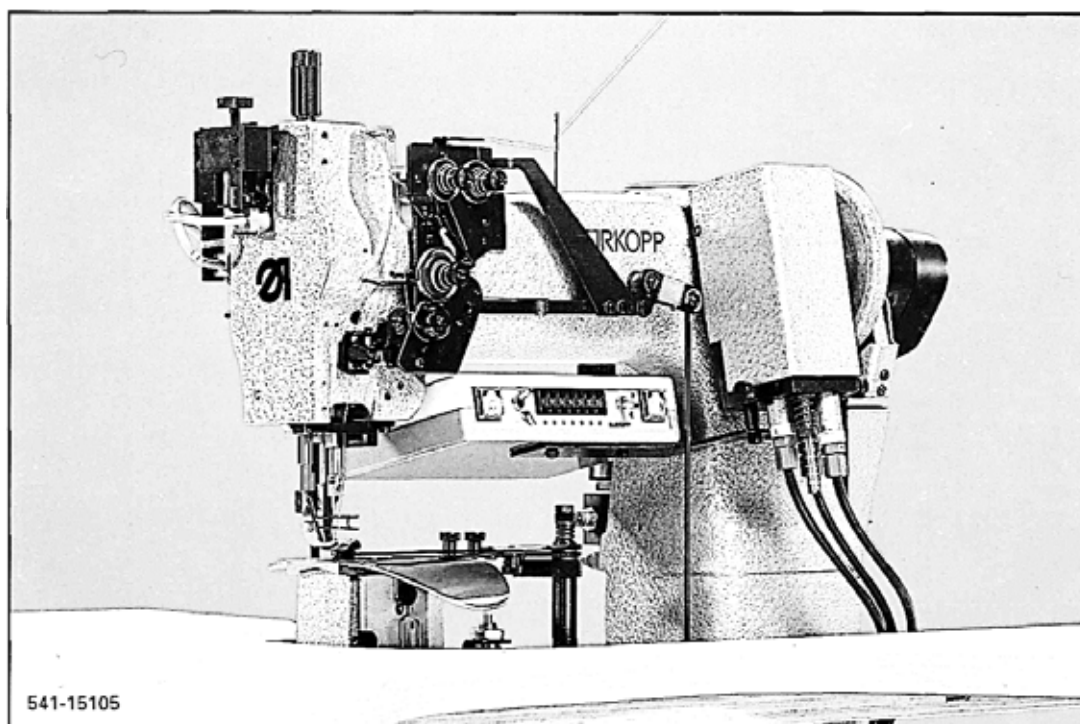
Внешний вид швейной машины марки 541–15105 фирмы «Дюркопп»
